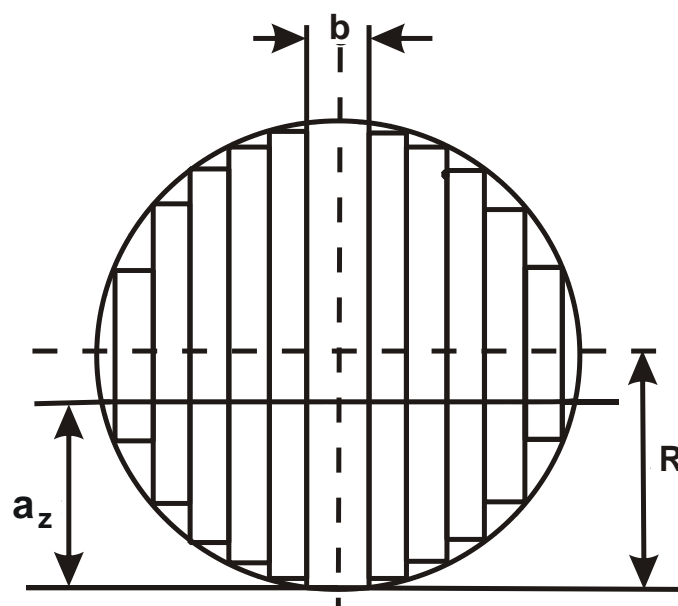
Розрахункова схема ріжучої частини зерна
